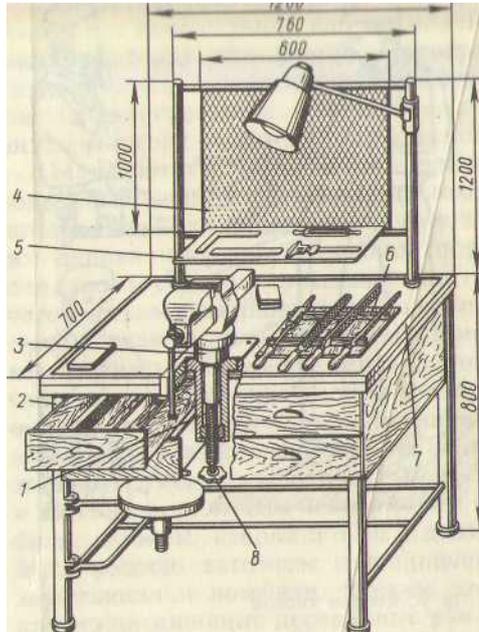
Рабочее место: 1—регулирующий винт; 2—каркас верстака; 3— хвостовик тисков; 4—защитная сетка; 5—полочка для измерительного инструмента; 6—планшет для рабочего инструмента; 7—планки-бортики; 8—маховичок
